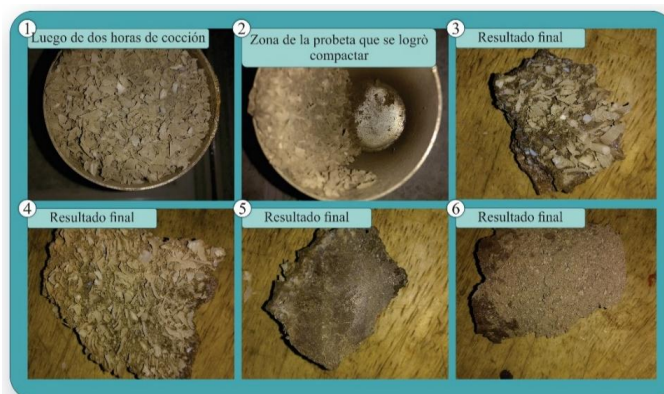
Proceso de desmoldado para compresión prueba N.º 2
